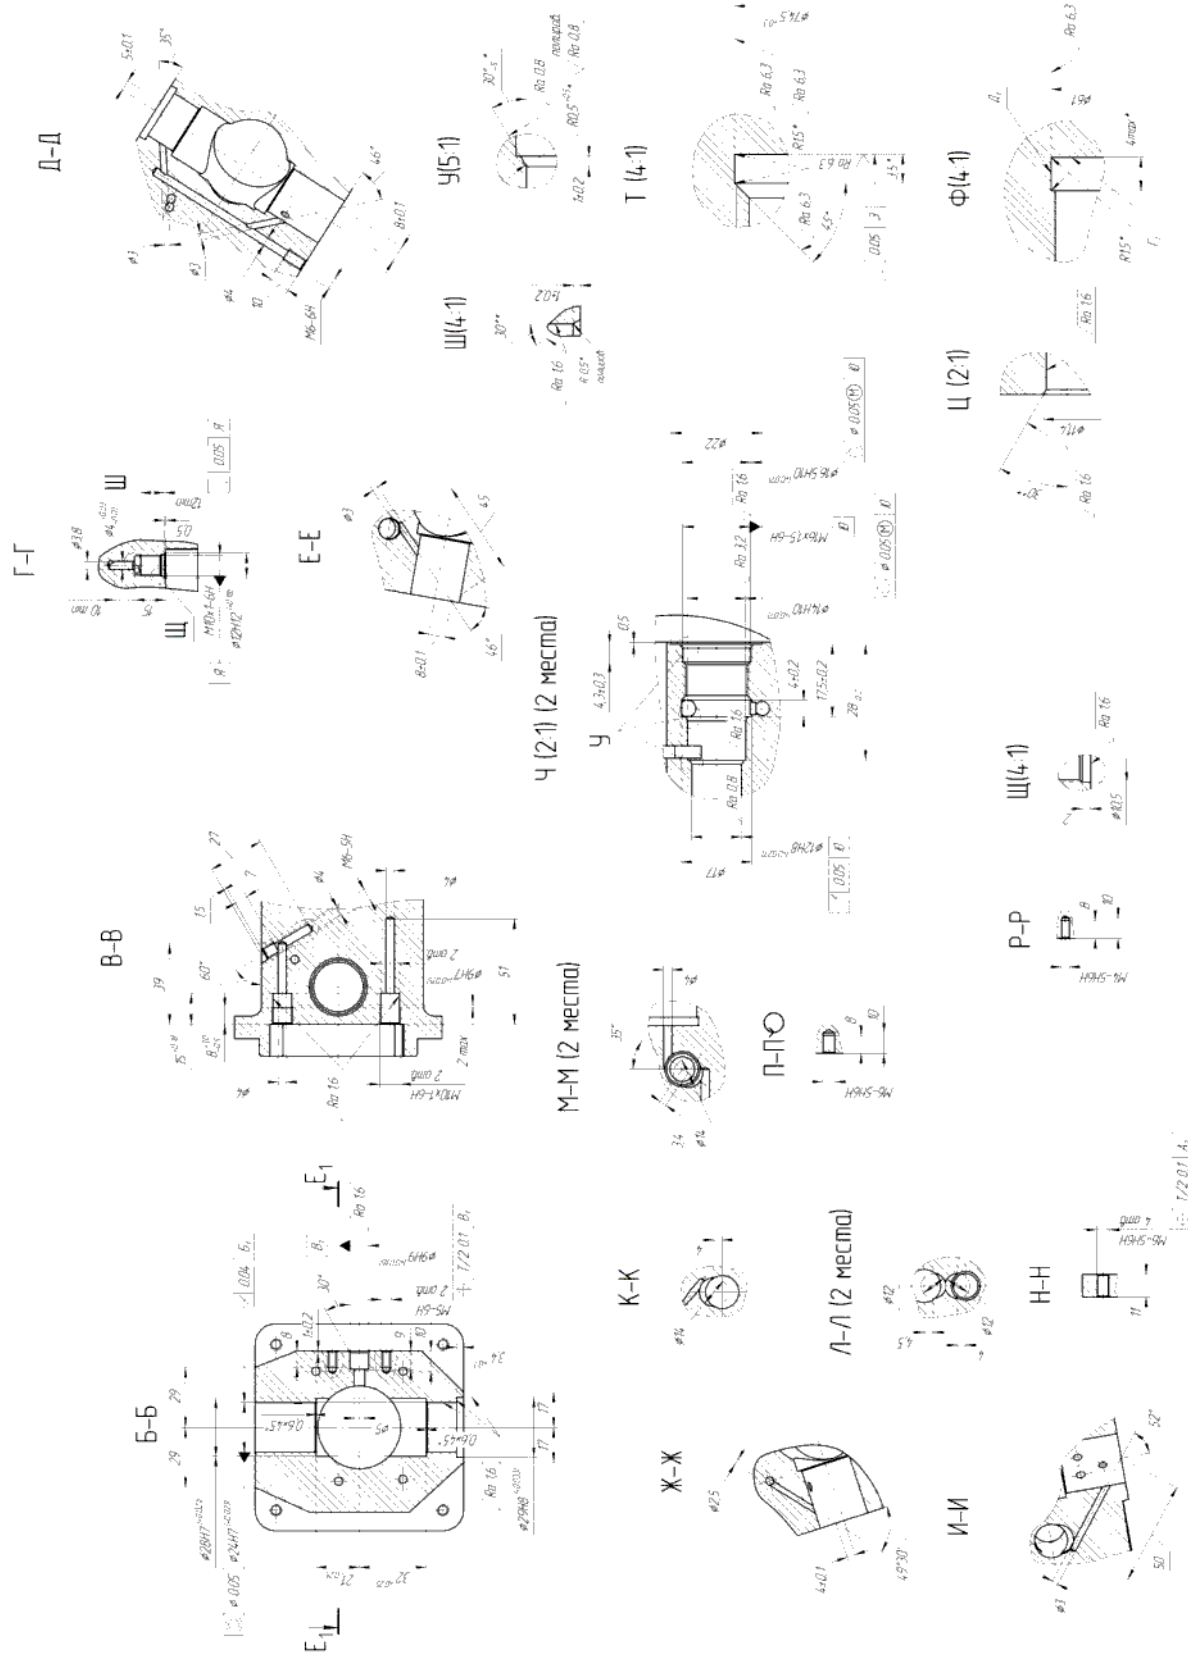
Конструкция корпуса гидроблока. Лист 2
